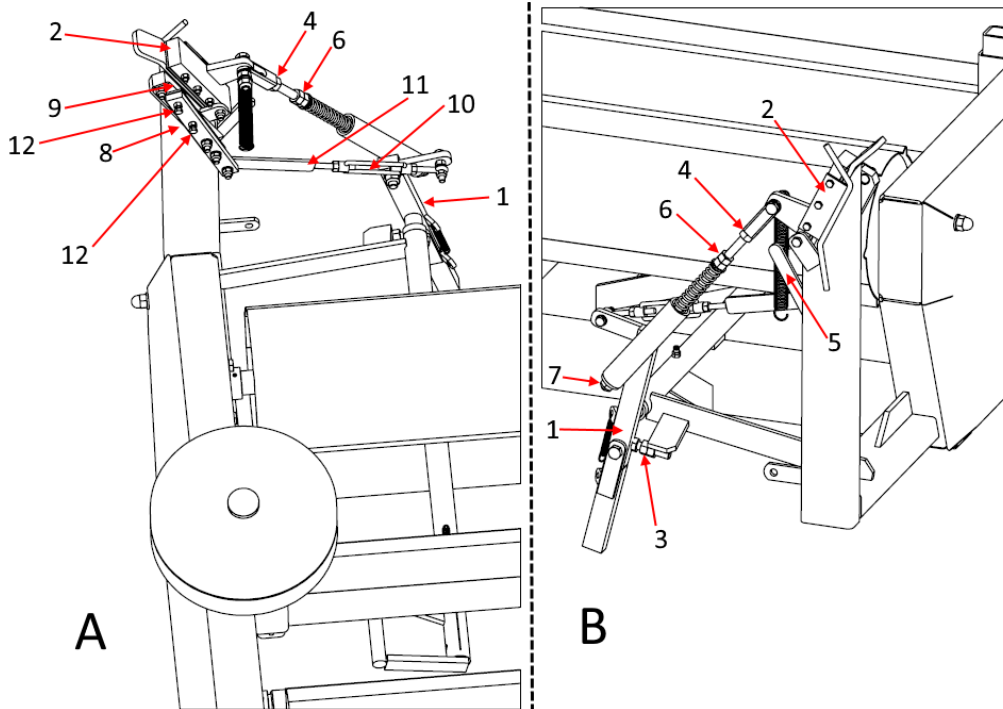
Coupe-film fermé : A – vue arrière, B – vue avant
